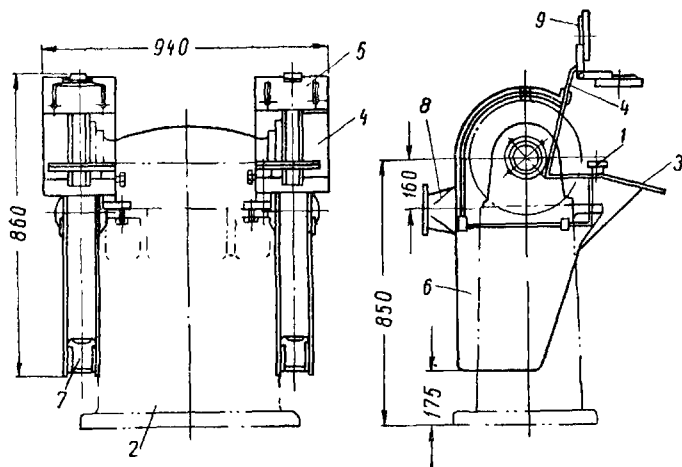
Отсос от обдирочно-шлифовального станка ЗМ-634
